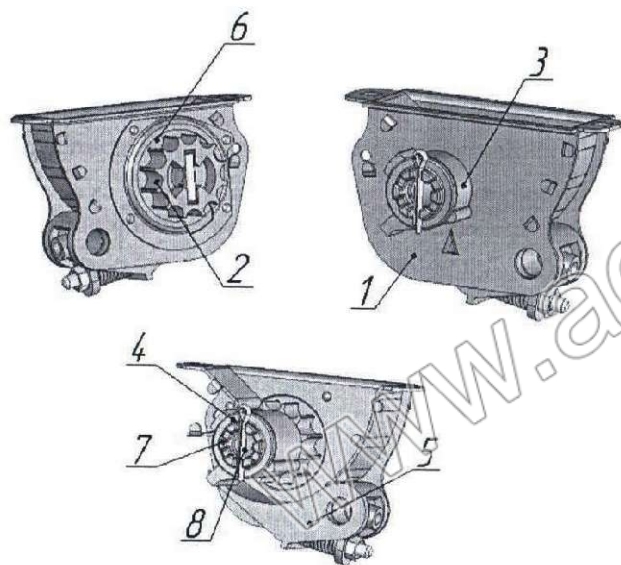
Зерновой высеваящий аппарат СКП 01.13.210
